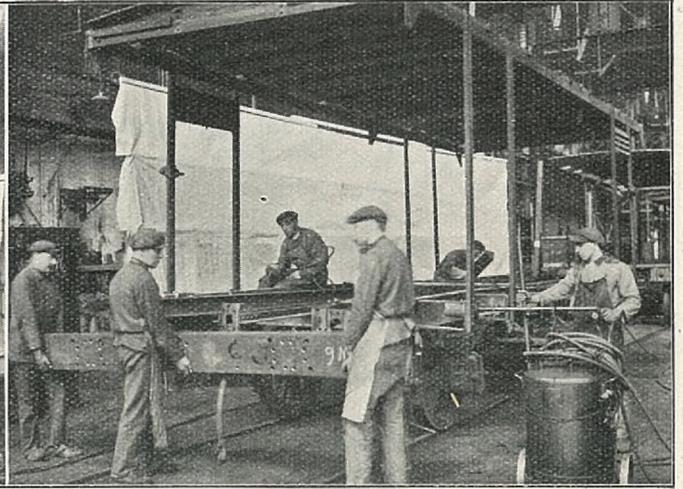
2<sup>me</sup> phase : Montage des traverses de tête, des montants d'angle, des goussets d'assemblage. Redressement des longerons. Achèvement des travaux de soudure.
